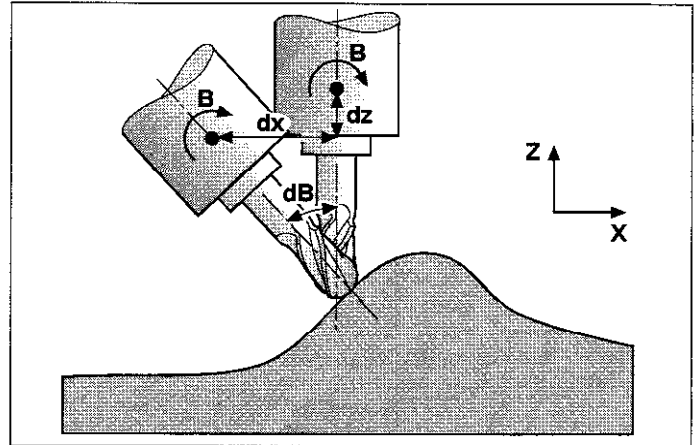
Versatz des Werkzeug-Bezugspunktes beim Schwenken des Werkzeugs
